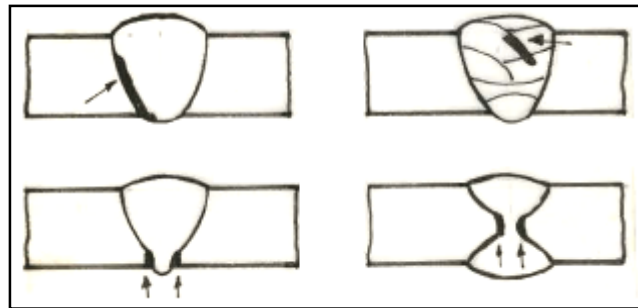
Diversas formas de falta de fusión en soldadura
